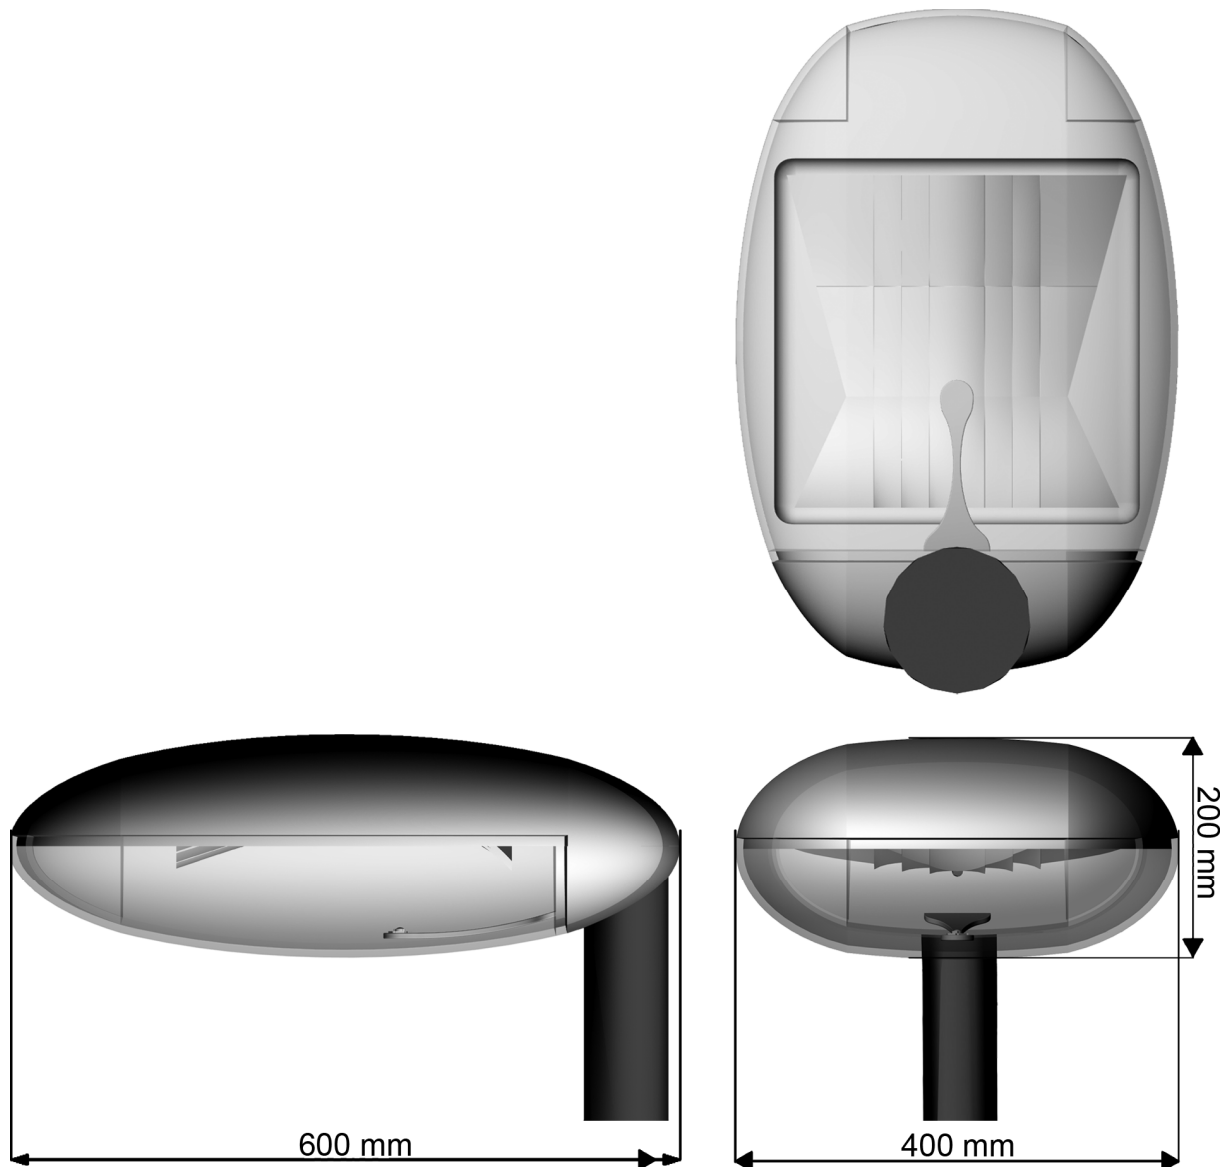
Außenmaße des Gehäuses in Millimetern
